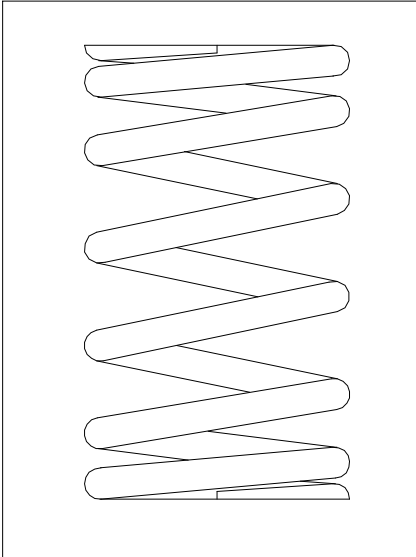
Zylindrische, progressive Schraubenfeder mit konstantem Drahtdurchmesser
